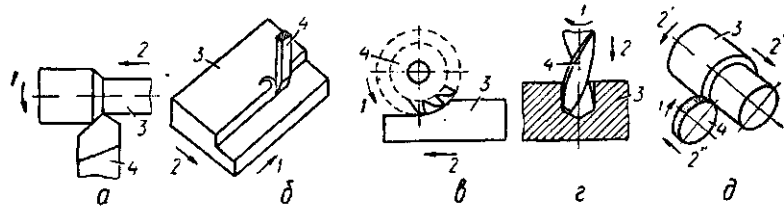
Типові способи обробки металів на металорізальних верстатах
